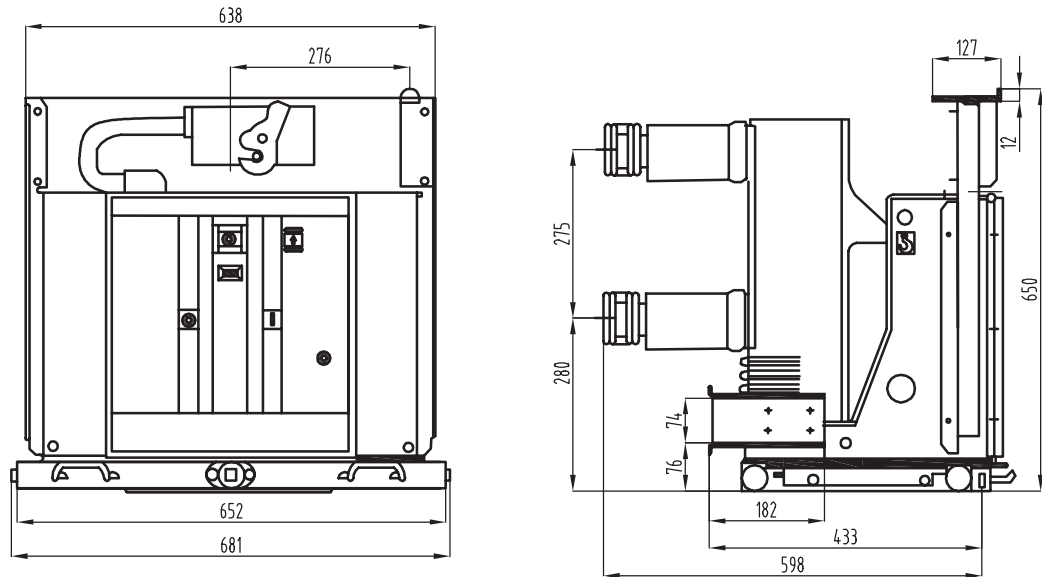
Габаритный размер выключателя ВВ выкатного исполнения для ячейки шириной 800 мм
